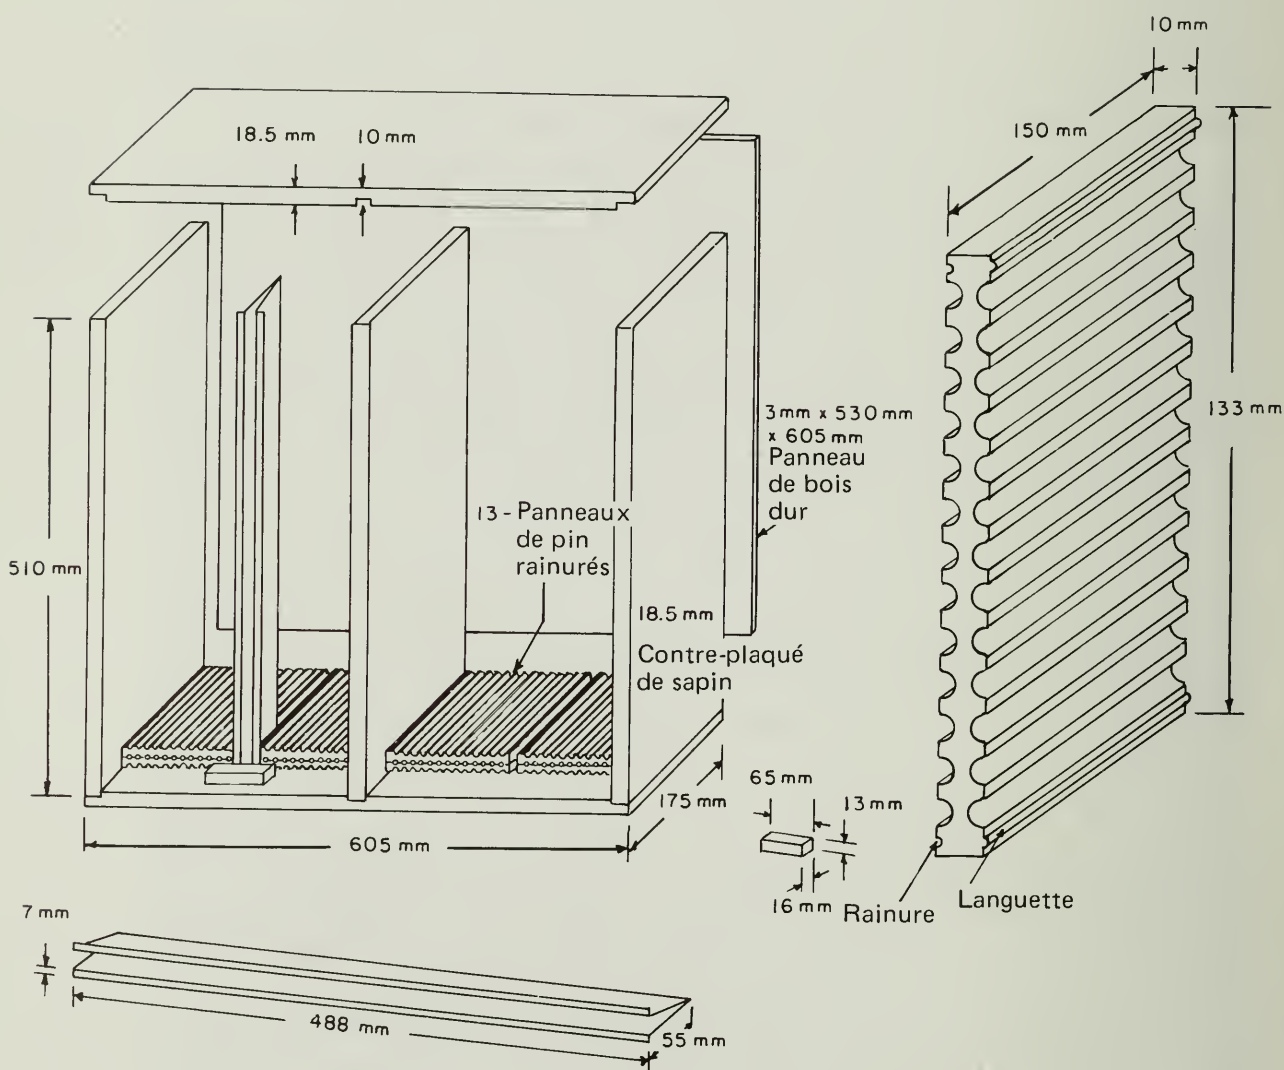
Plan d'une ruche faite de panneaux de pin à 13 tunnels et d'un diviseur en métal.
